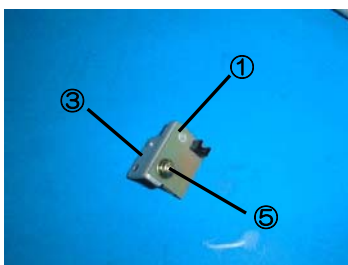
Gap Sensor Board、Cable Sensor Head Gap (その 2)
